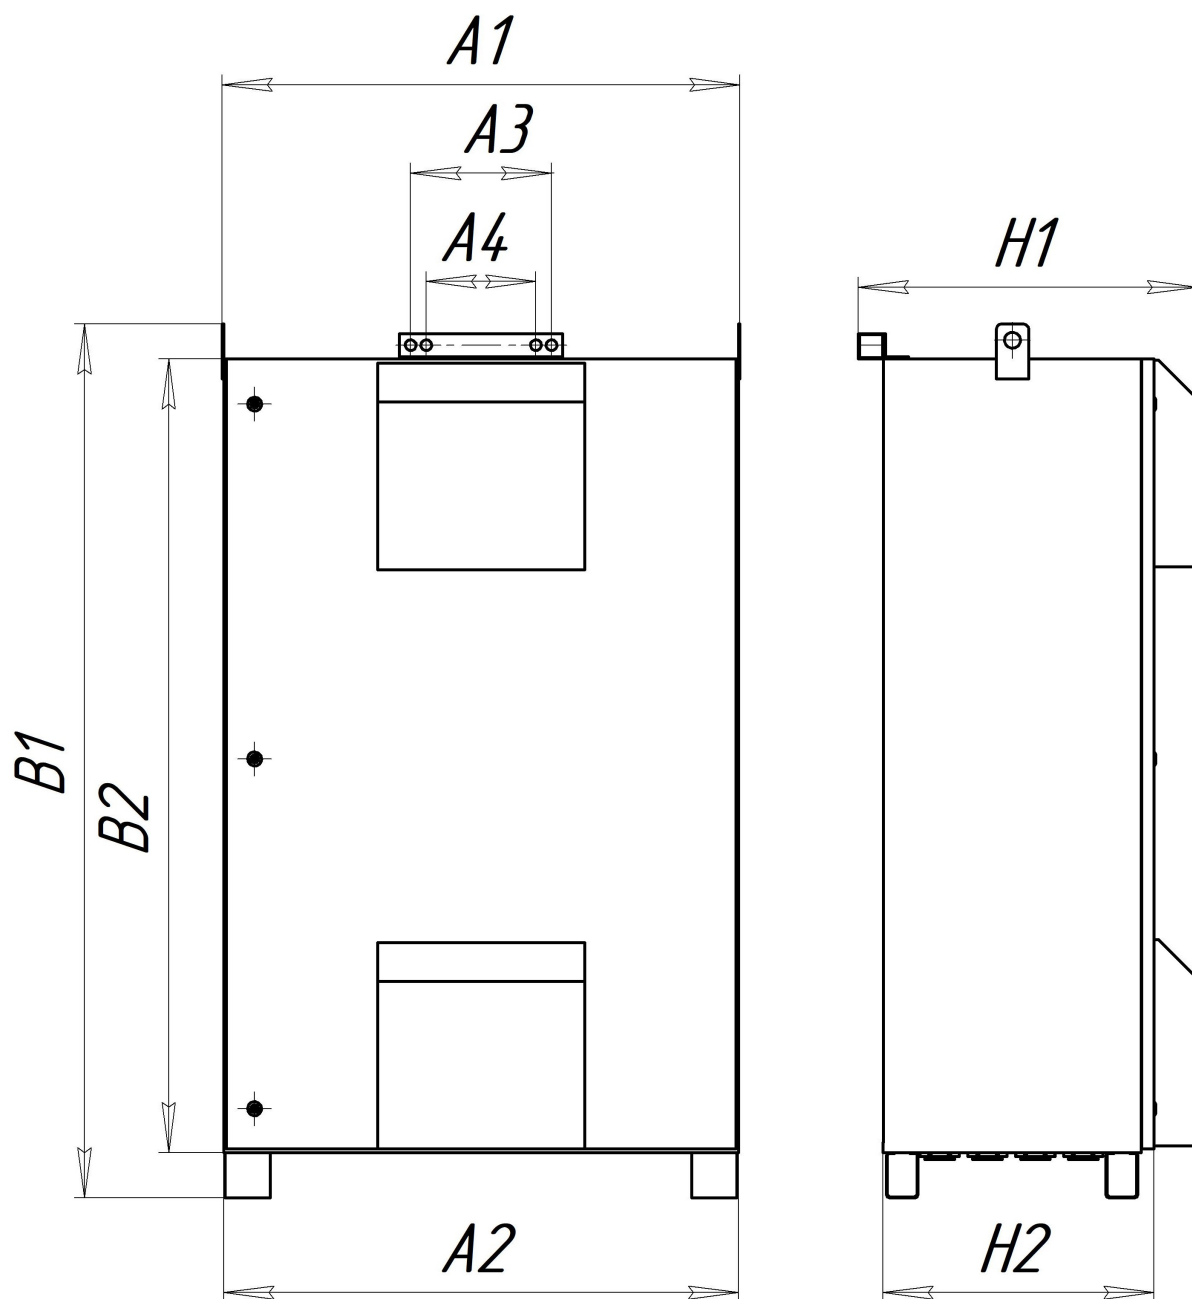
Габаритные и присоединительные размеры УАБН-3
